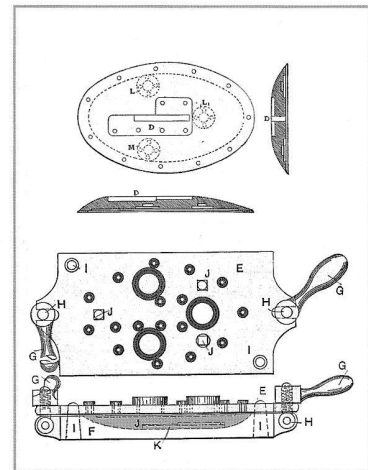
Aluminium-Fussplatte eines elektrischen Tuschneidegerätes, darunter die zugehörige Bohrschablone mit 20 Bohrbuchsen. (Quelle: Joseph V. Woodworth, American Tool Making and Interchangeable Manufacturing, New York 1917; S. 93, Fig. 82 u. 83, Bohrbuchsen und Werkstück grau angelegt)
